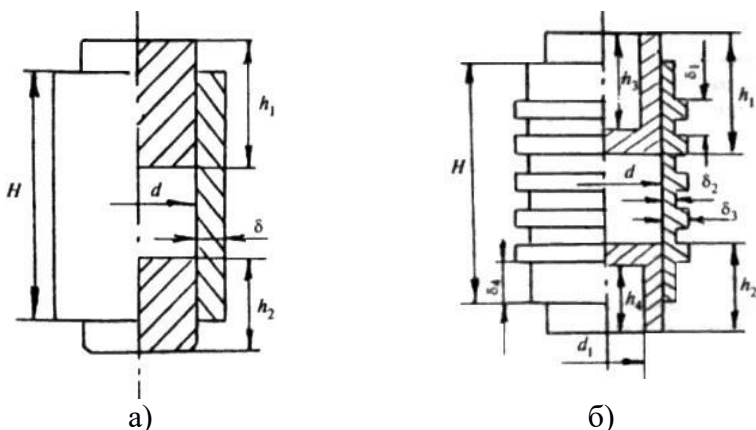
Формы для изготовления цилиндрических образцов:
